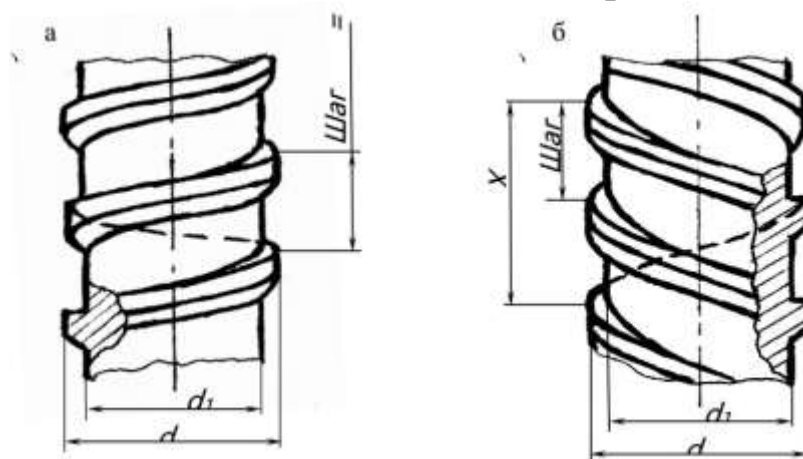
Шаг резьбы однозаходной и многозаходной резьбы
